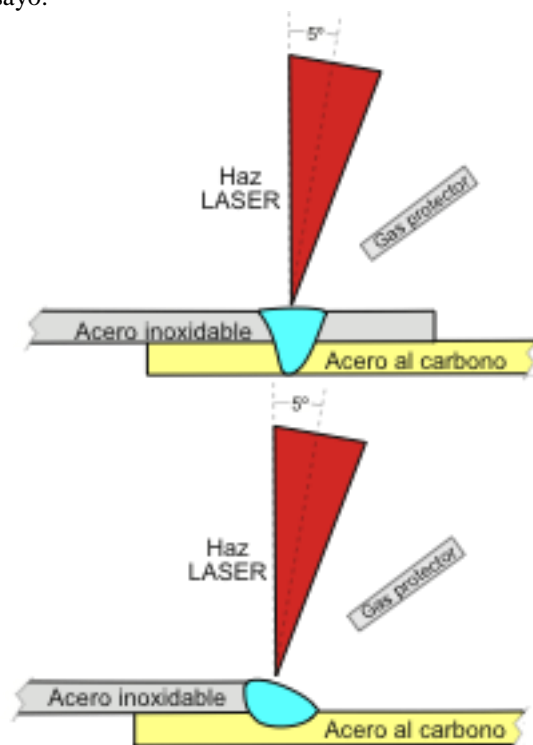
Configuraciones de soldadura láser: a tope (arriba) y en esquina (abajo).
